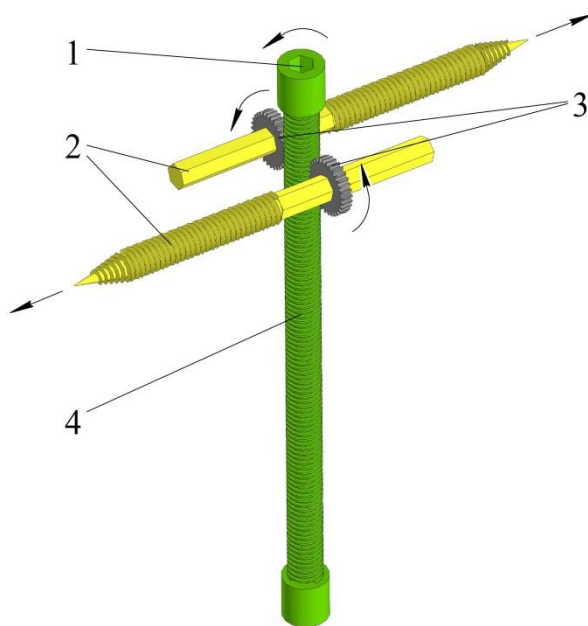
Устройство червячной передачи внутри ножки эндопротеза: 1 – отверстие вала червячной передачи для шестигранной отвертки, 2 – винты, 3 – зубчатые колеса, 4 – вал червячной передачи.
